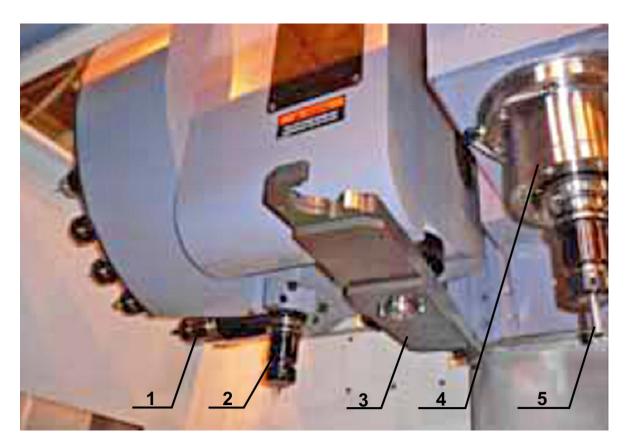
Инструментальный магазин типа «PYKA» (вид со стороны манипулятора): I — инструмент в магазине в штатном положении; 2 — инструмент на подготовительной позиции; 3 — манипулятор в штатном положении; 4 — шпиндель; 5 — инструмент в шпинделе
